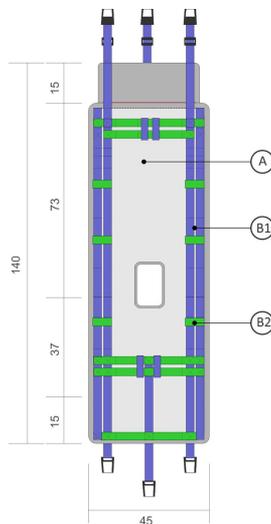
Vista superior de pieza flexible. Incluye dimensiones y detalle de grupos de componentes.
